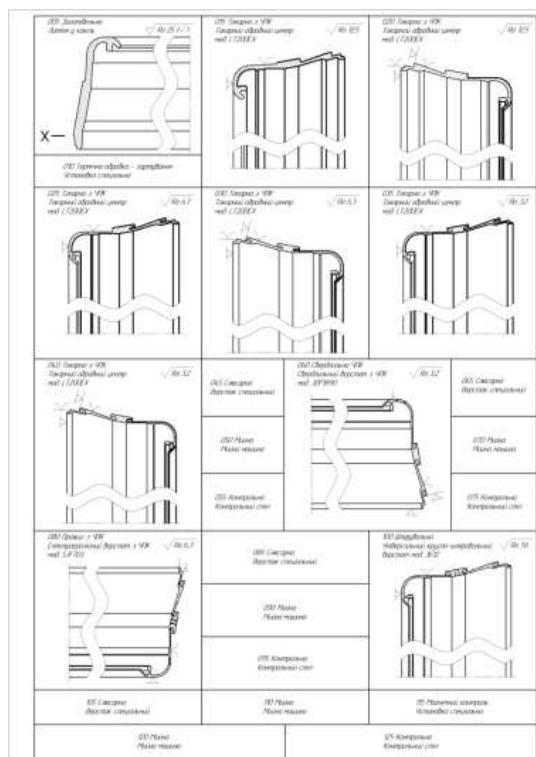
Ескіз маршруту виготовлення деталі
